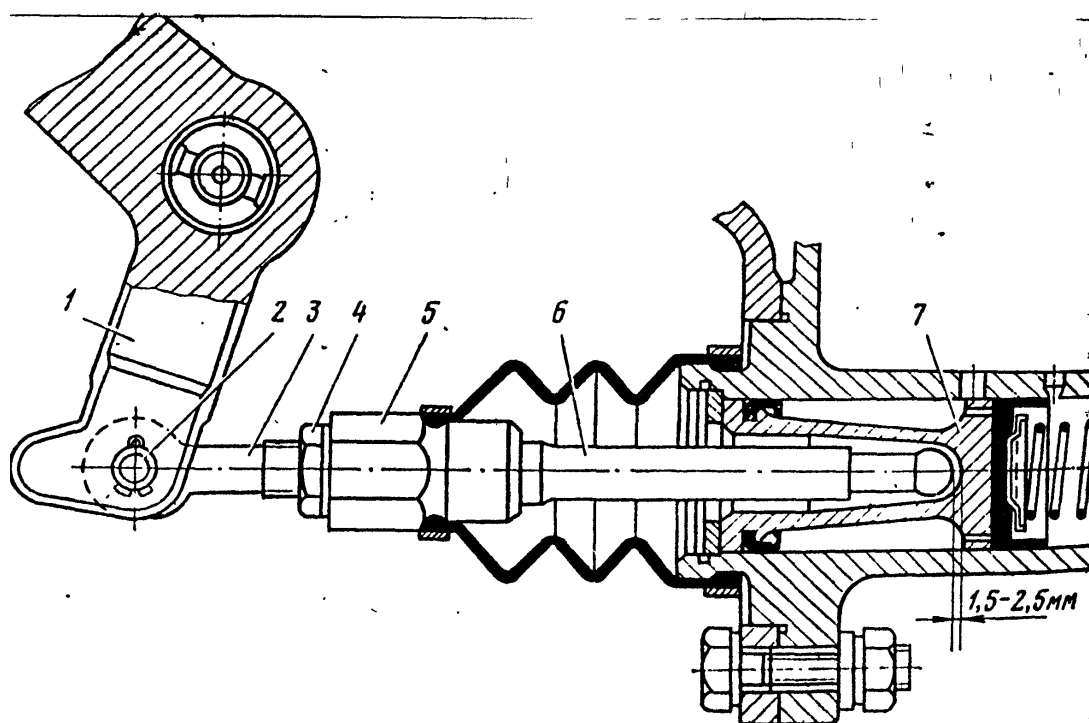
Главный цилиндр гидравлического привода тормозов
